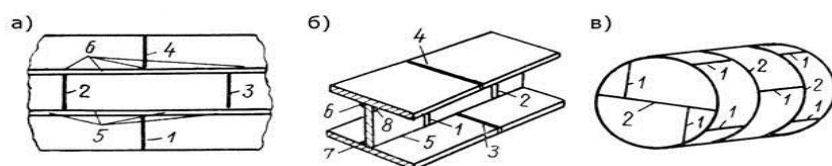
Последовательность наложения швов (1-8) при сварке:
